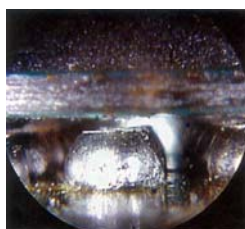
Отрыв вывода корпуса BGA от поверхности компонента
